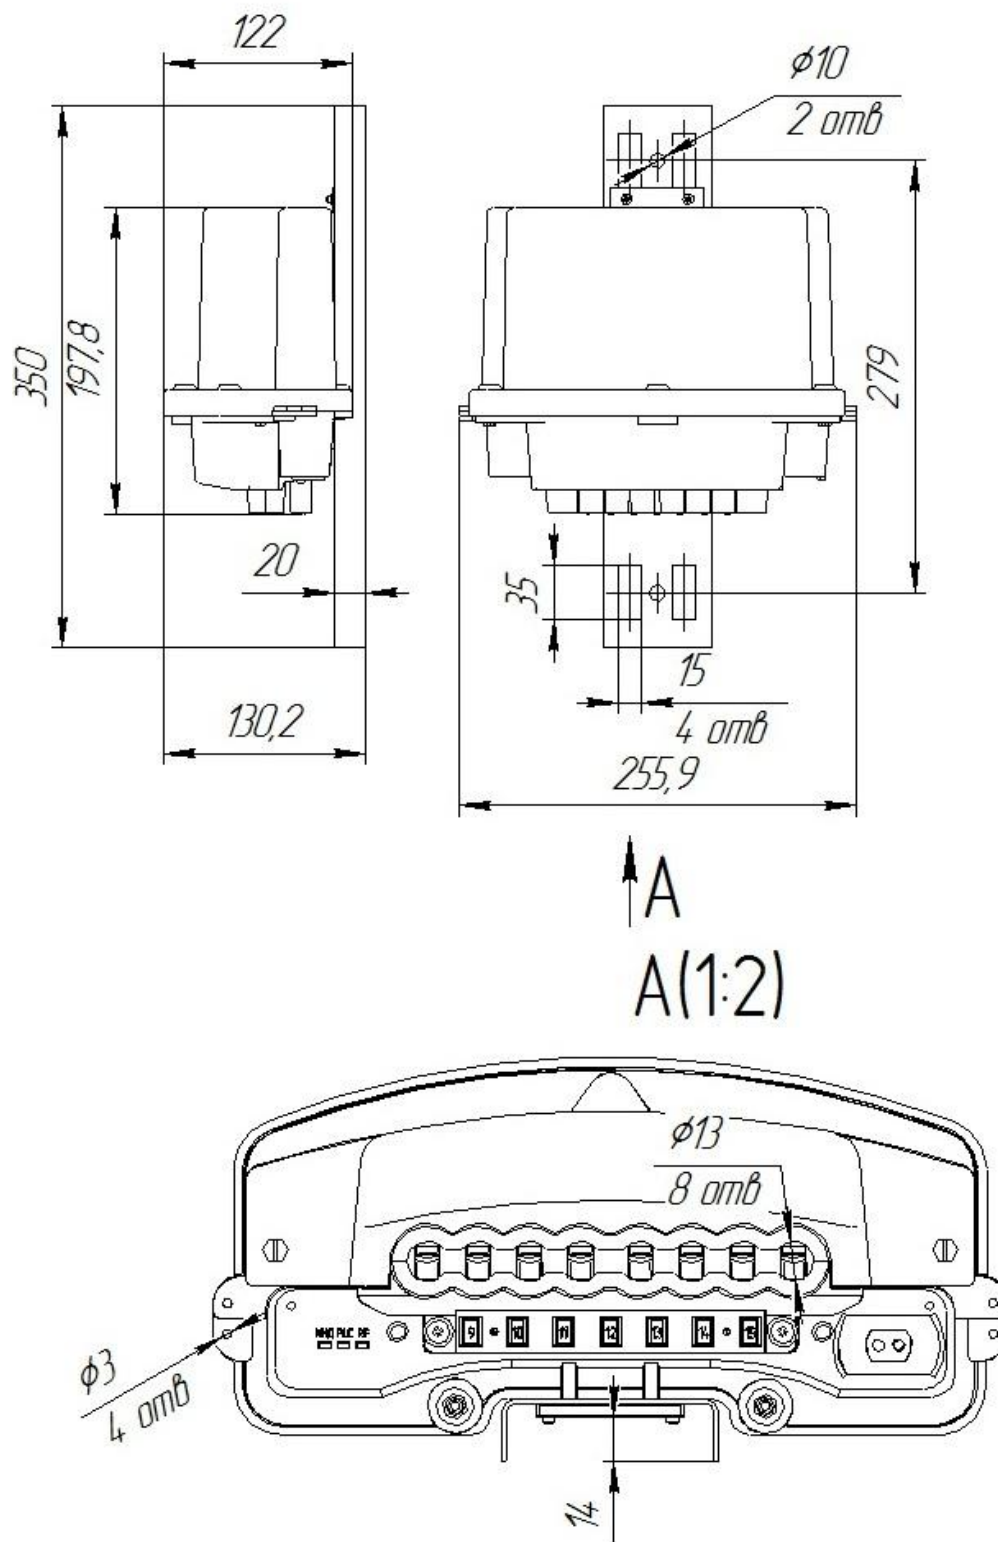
Габаритный чертеж и установочные размеры счетчиков МАЯК 302АРТН
